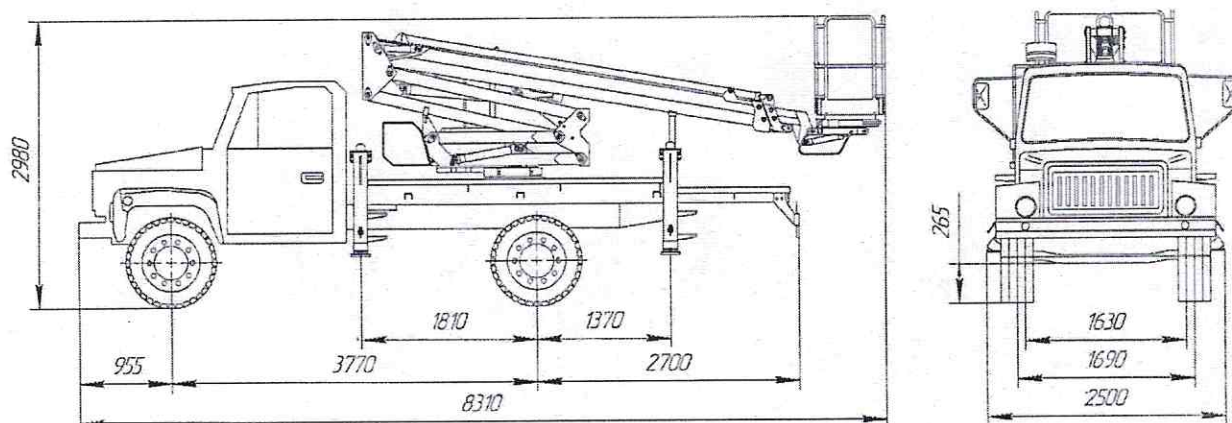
Габаритные размеры подъемника ВИПО-20-01
